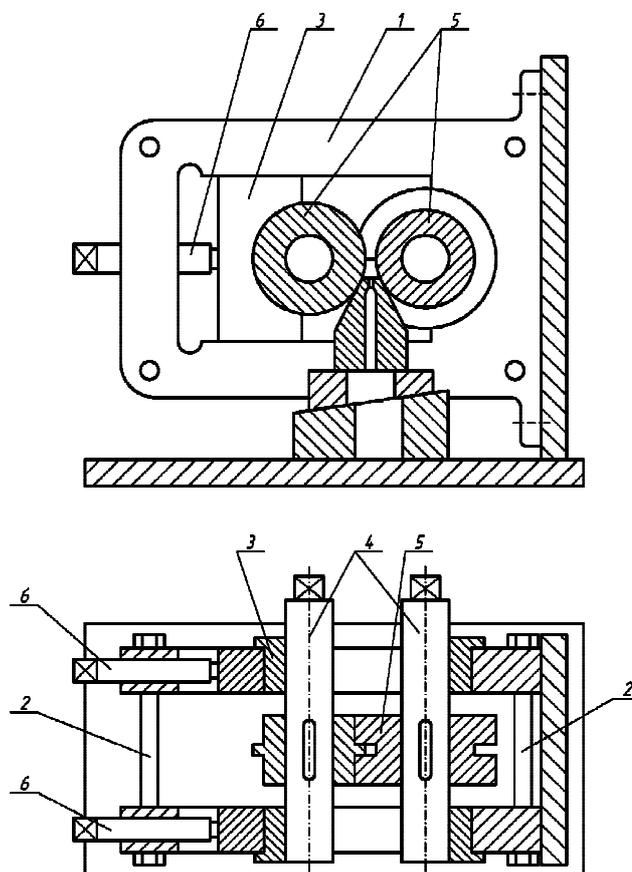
Лабораторная установка для совмещенной прокатки-прессования алюминиевых сплавов на базе прокатного стана ДУО200
